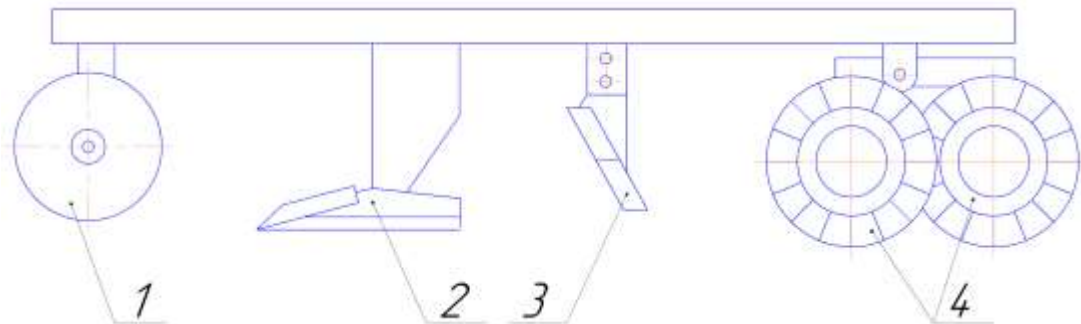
Схема розташування робочих органів комбінованого агрегату типу АКП - 5
